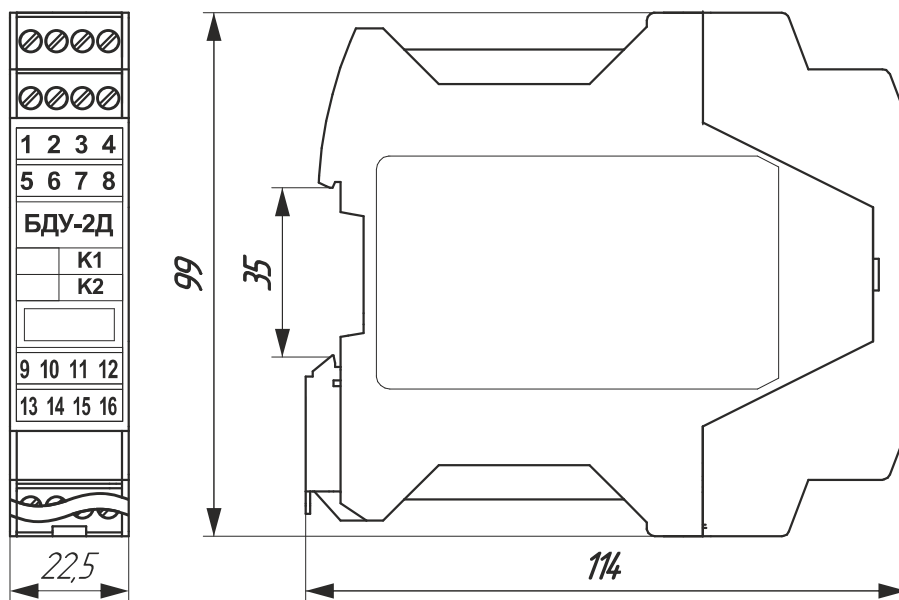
Внешний вид и габаритные размеры корпуса блока в исполнении БДУ-хД.3хх
